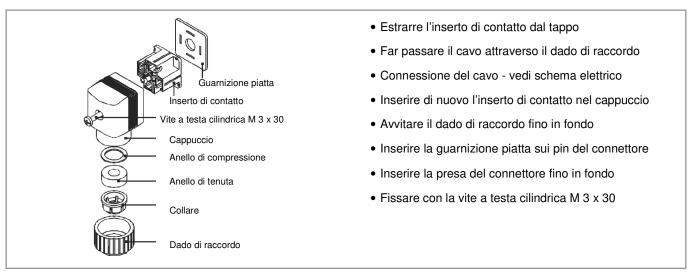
Montaggio del connettore Bürkert 8376 per la valvola zavorra di gas
